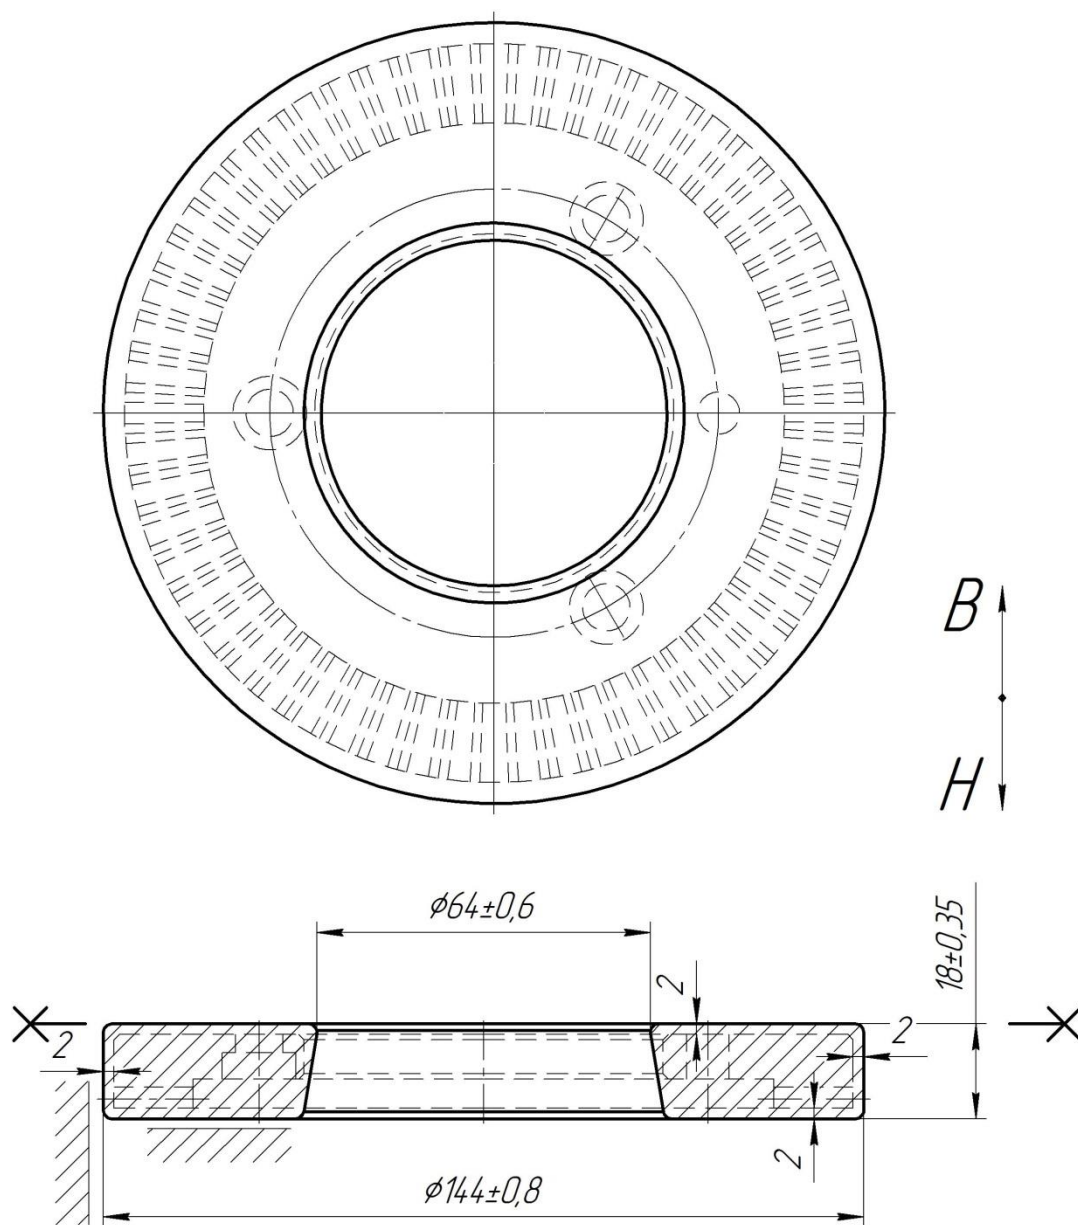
Общий вид заготовки детали - «Храповик»
